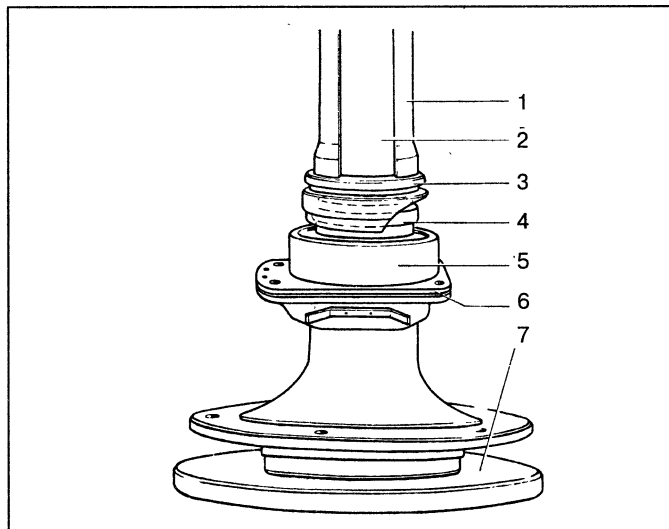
Запрессовка запорного кольца подшипника полуоси: 1 – оправка; 2 – полуось; 3 – обойма; 4 – запорное кольцо; 5 – подшипник; 6 – пластина крепления подшипника и маслоотражатель в сборе; 7 – опорное кольцо
